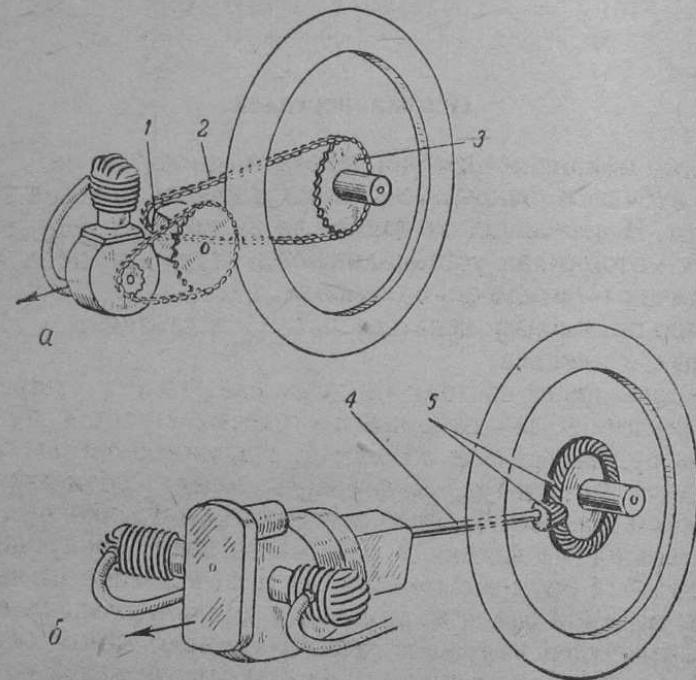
Передача усилия от коробки передач на ведущее колесо при цепной и карданной передачах:
